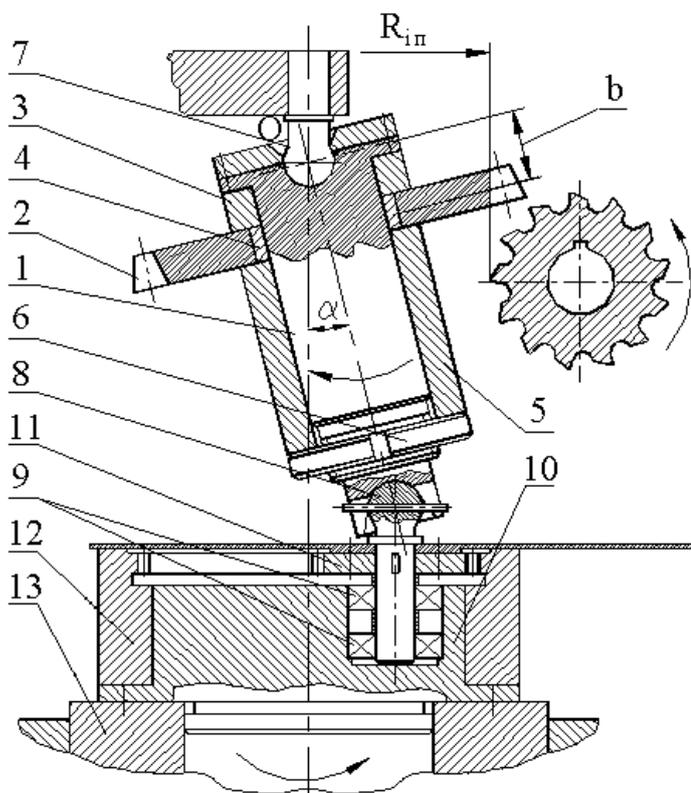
Приспособление для обработки зубьев сателлита прецессионной передачи
